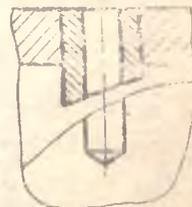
Специальная кондукторная втулка для сверления отверстия на криволинейной поверхности
